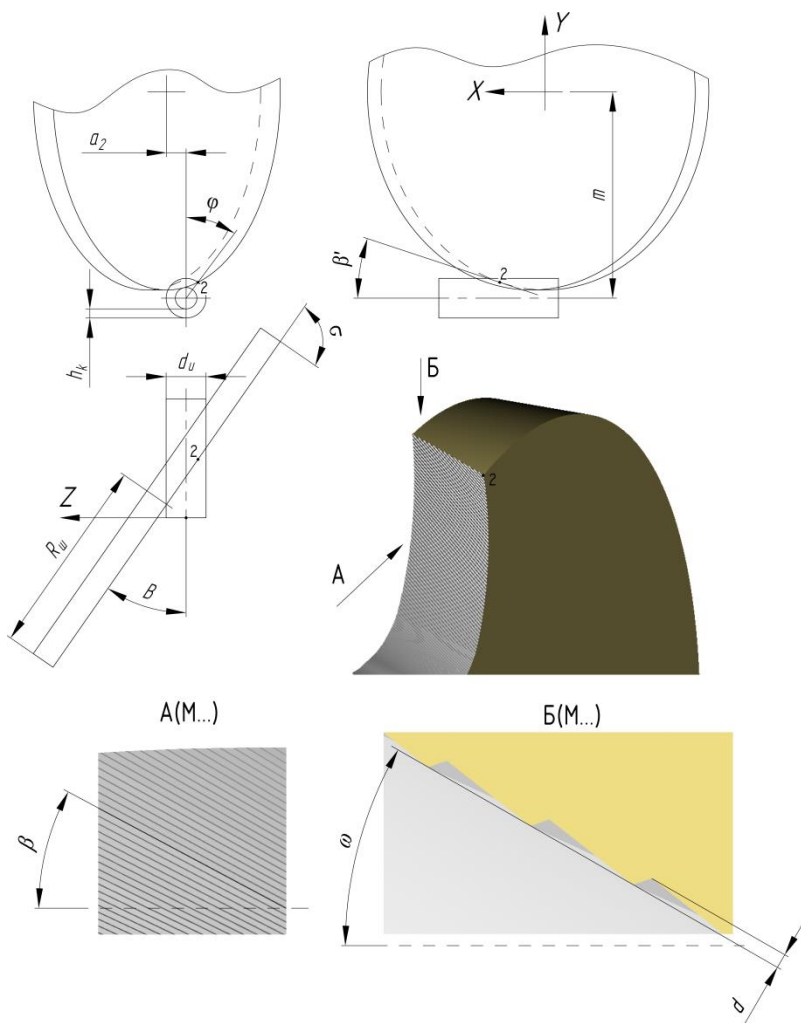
Расчетная схема определения шероховатости винтовой передней поверхности режущего инструмента
